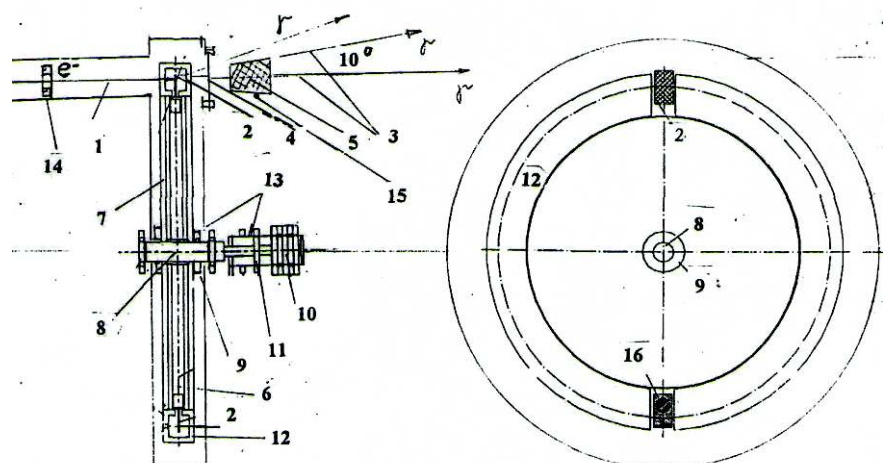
Обертаючийся конвертор електронного пучка (1 - електронний пучок, 2 - пластини танталового конвертера, 3 - фотонний пучок, 4 - вихідна фольга прискорювача, 5 - мішень, 6 - титановий диск, 7 - кожух диска, 8 - валець обертання, 9 - підшипники, 10 - ввід обертання, 11 - датчик обертання, 12 - охолодження кожуха, 13 - вакуумна камера, 14 - датчик положення електронного пучка, 15 - датчик температури мішені, 16 - болометричний датчик)
